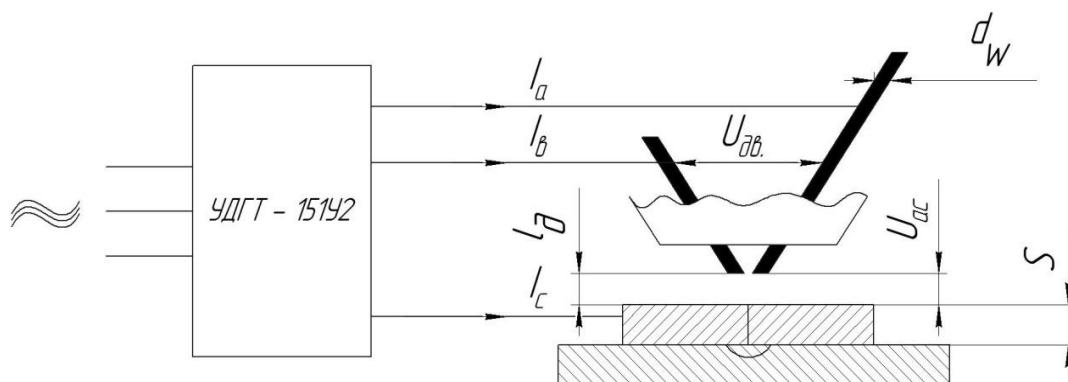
Схема сварочного поста для сварки 3-х фазной свободной дугой неплавящимися электродами в среде защитного газа
